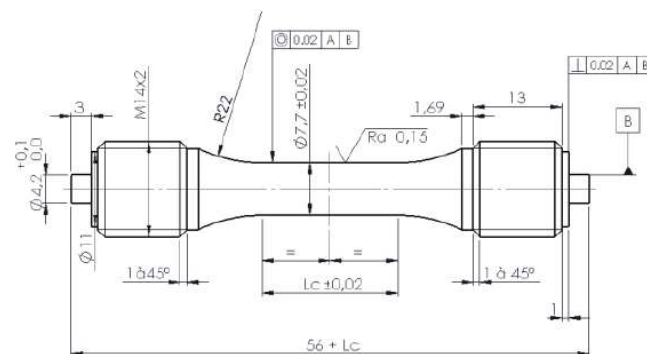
Géométrie de l'éprouvette utilisée dans les essais de fatigue uniaxiale
